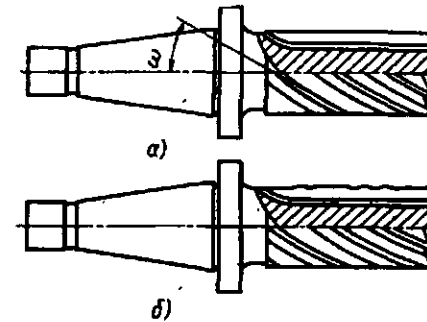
Концевая фреза с винтовыми твердосплавными пластинами: а — чистовая; б — черновая
